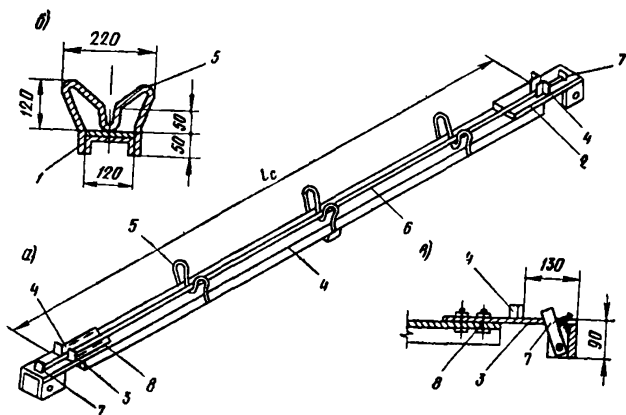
Кондуктор для приварки коротышей на концах стержня
